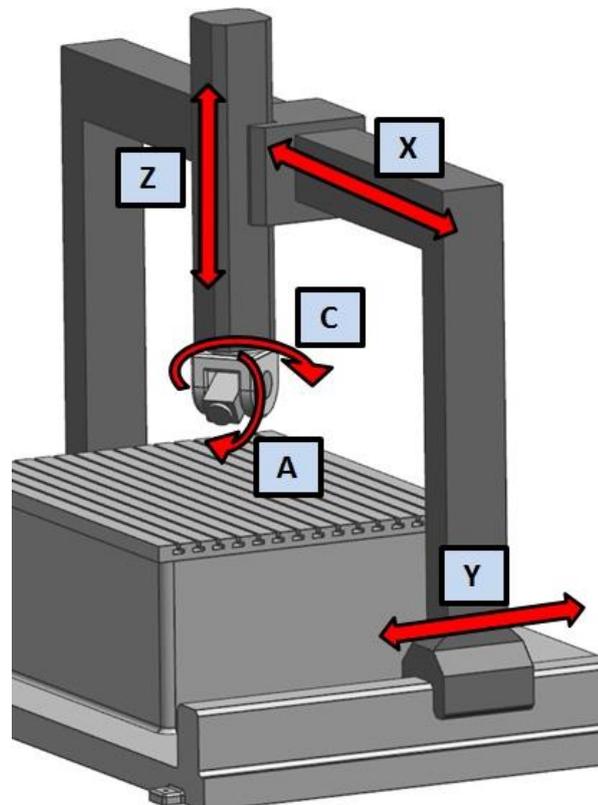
Кинематика 5-ти координатного ОЦ с поворотной фрезерной головкой (оси А и С)
